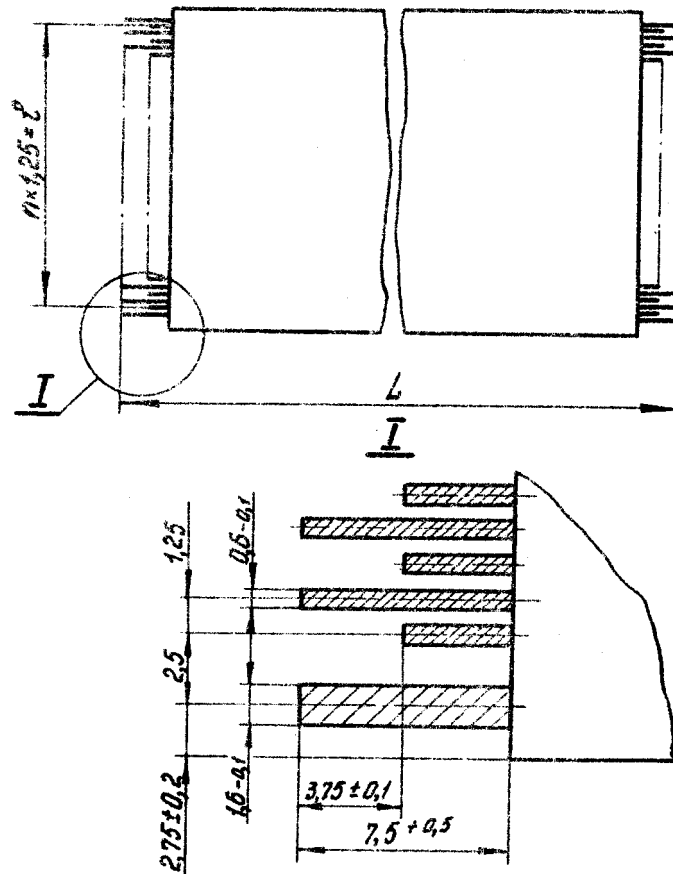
Гибкий печатный кабель с двухрядными контактными лепестками.
